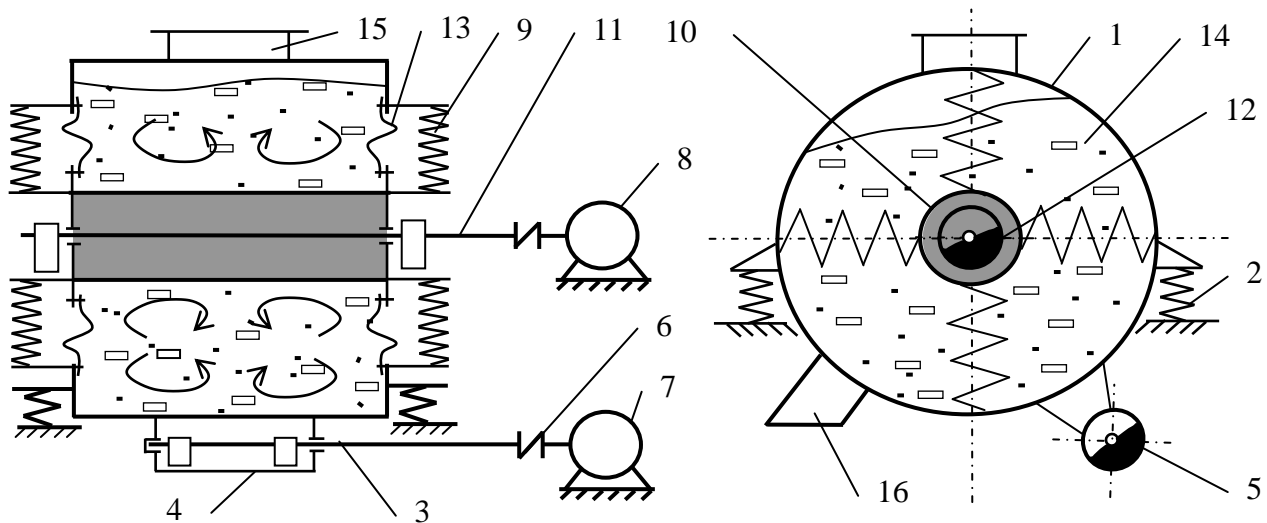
Вібраційна машина з дебалансним активатором руху робочого середовища: 1 – робоча камера; 2 – пружні опори робочої камери; 3 – вал віброзбуджувача робочої камери; 4 – віброзбуджувач робочої камери; 5 – дебаланси вібропривода робочої камери; 6 – муфта еластична; 7 – електродвигун вібропривода робочої камери; 8 – електродвигун вібропривода активатора; 9 – підвіска активатора; 10 – активатор; 11 – вал віброзбуджувача активатора; 12 – дебаланси активатора; 13 – еластичні стінки робочої камери; 14 – робоче середовище з оброблюваними деталями; 15 – завантажувальна горловина; 16 – вивантажувальна горловина
